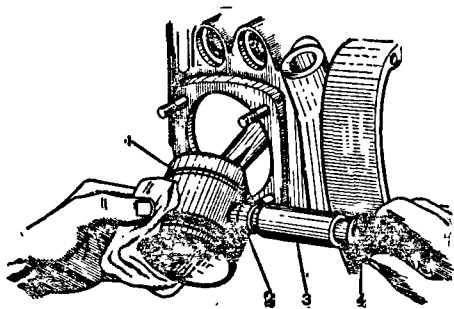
Установка поршневого пальца в поршень и головку шатуна:
